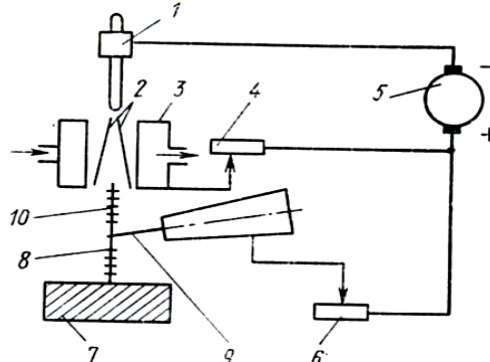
Схема установки для плазменной наплавки проволокой или стержнем:
